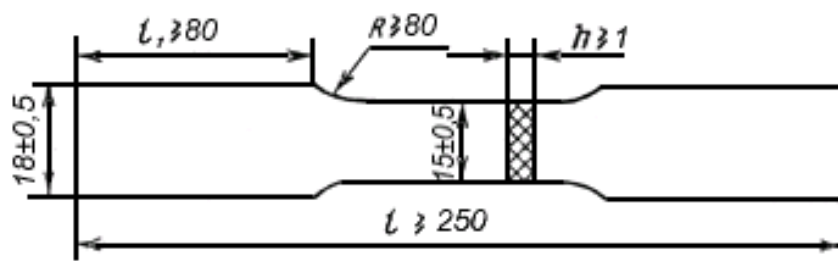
Эскиз образца в виде двусторонней лопатки для испытаний на одноосное растяжение с размерами, выполненными по ГОСТ 25.601-80
